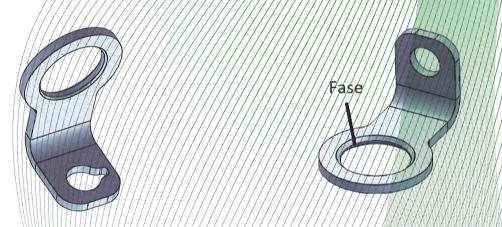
Kurvenhalterung, Typ: TS-Lasche (TS-011) (mit Sollbruchstelle, mit 45° Fase oder ohne Fase)
